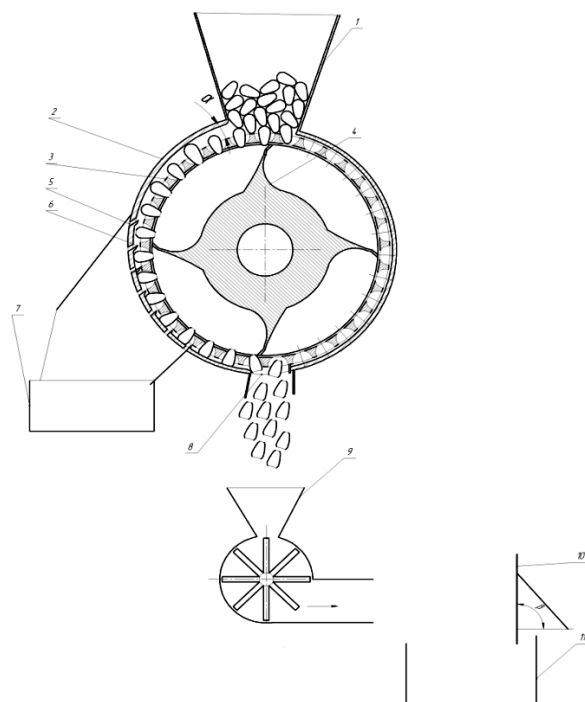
Барабанно-фрезерный механизм устройства в разрезе:
